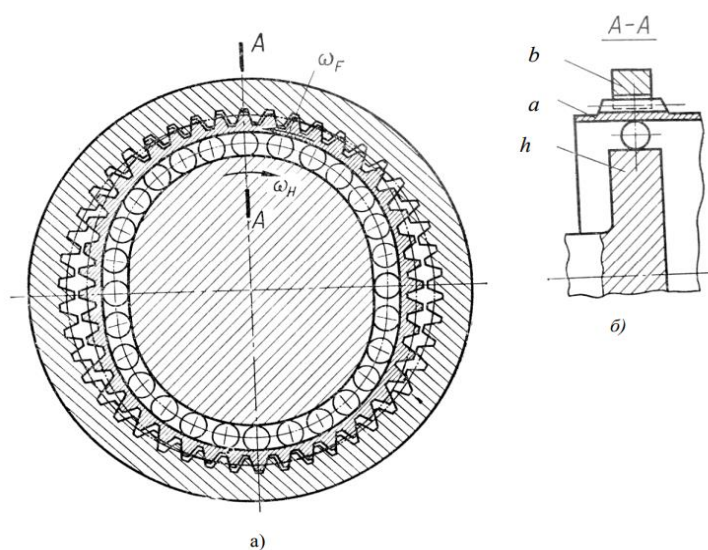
Конструкция волновой передачи с генератором волн в виде гибкого подшипника
